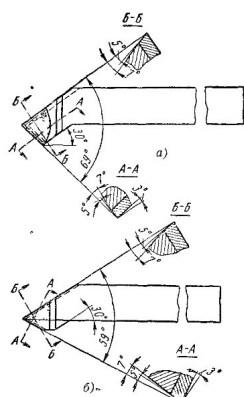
Резьбовые резцы для наружной метрической резьбы токаря В.М. Бирюкова:
